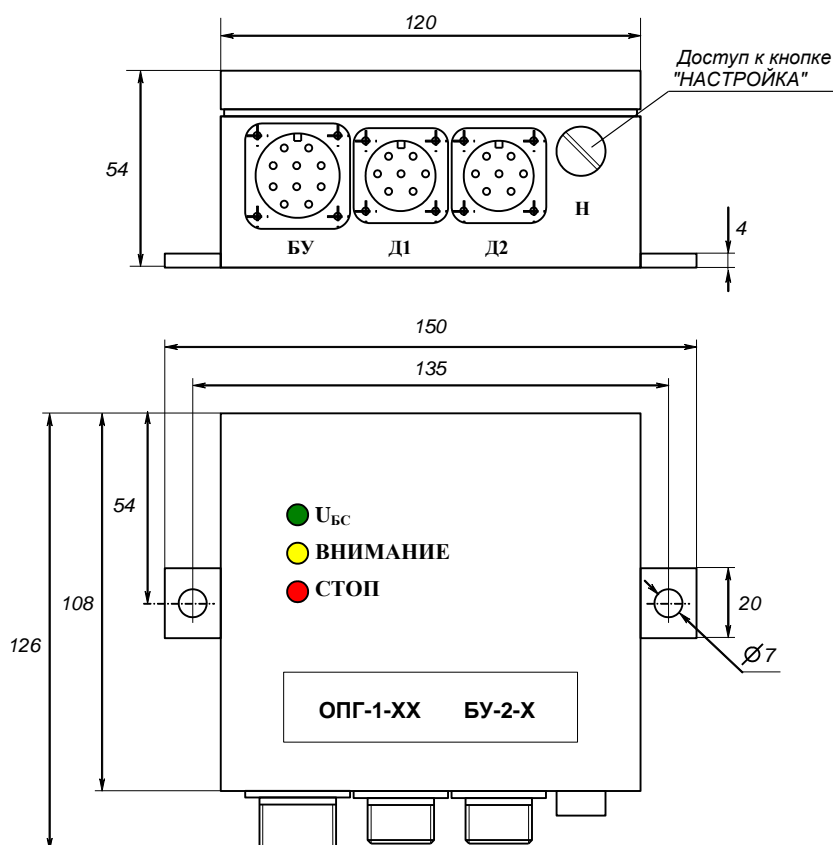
Габаритные и присоединительные размеры БУ-2
